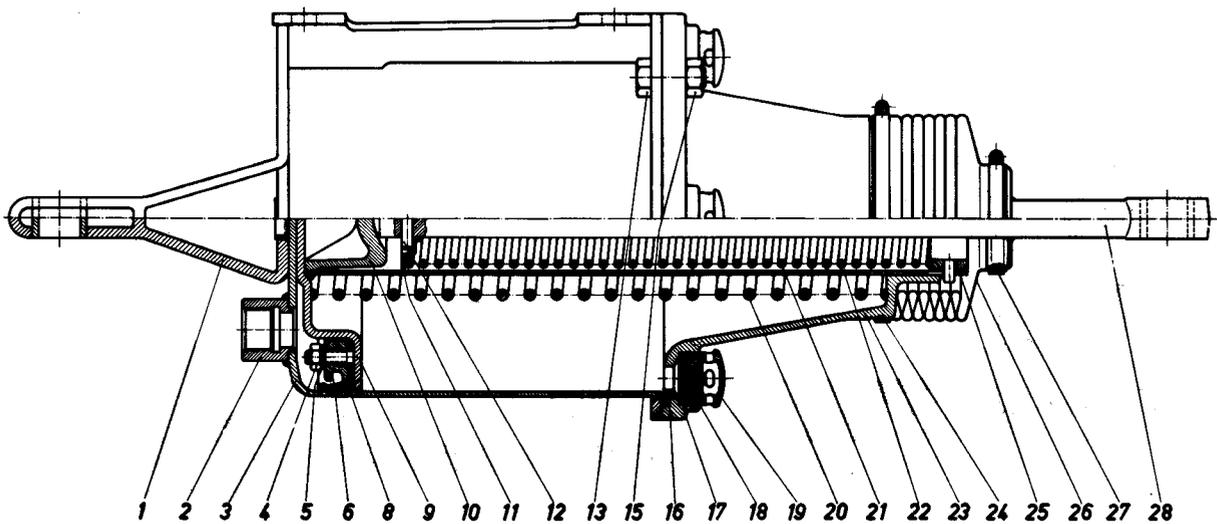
Schnitt sandgeschützter Bremszylinder mit innenliegender Gestängerückdruckfeder
